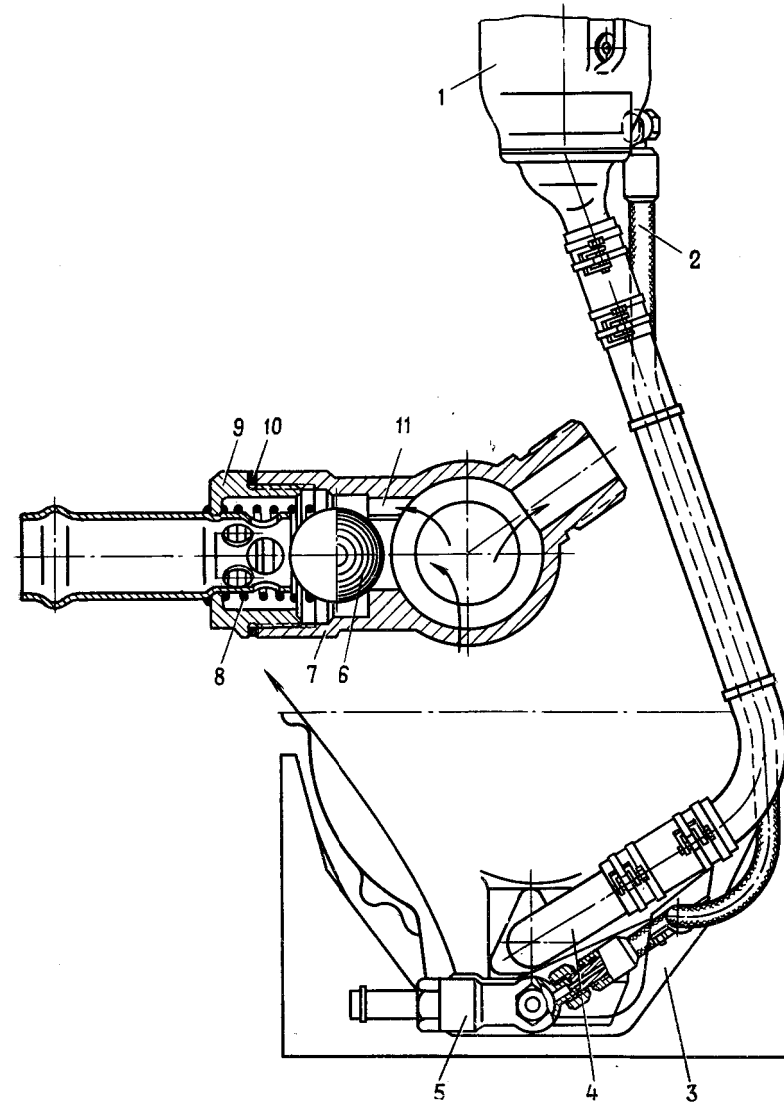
Установка масляного центробежного фильтра МЦ-1 в танке:
